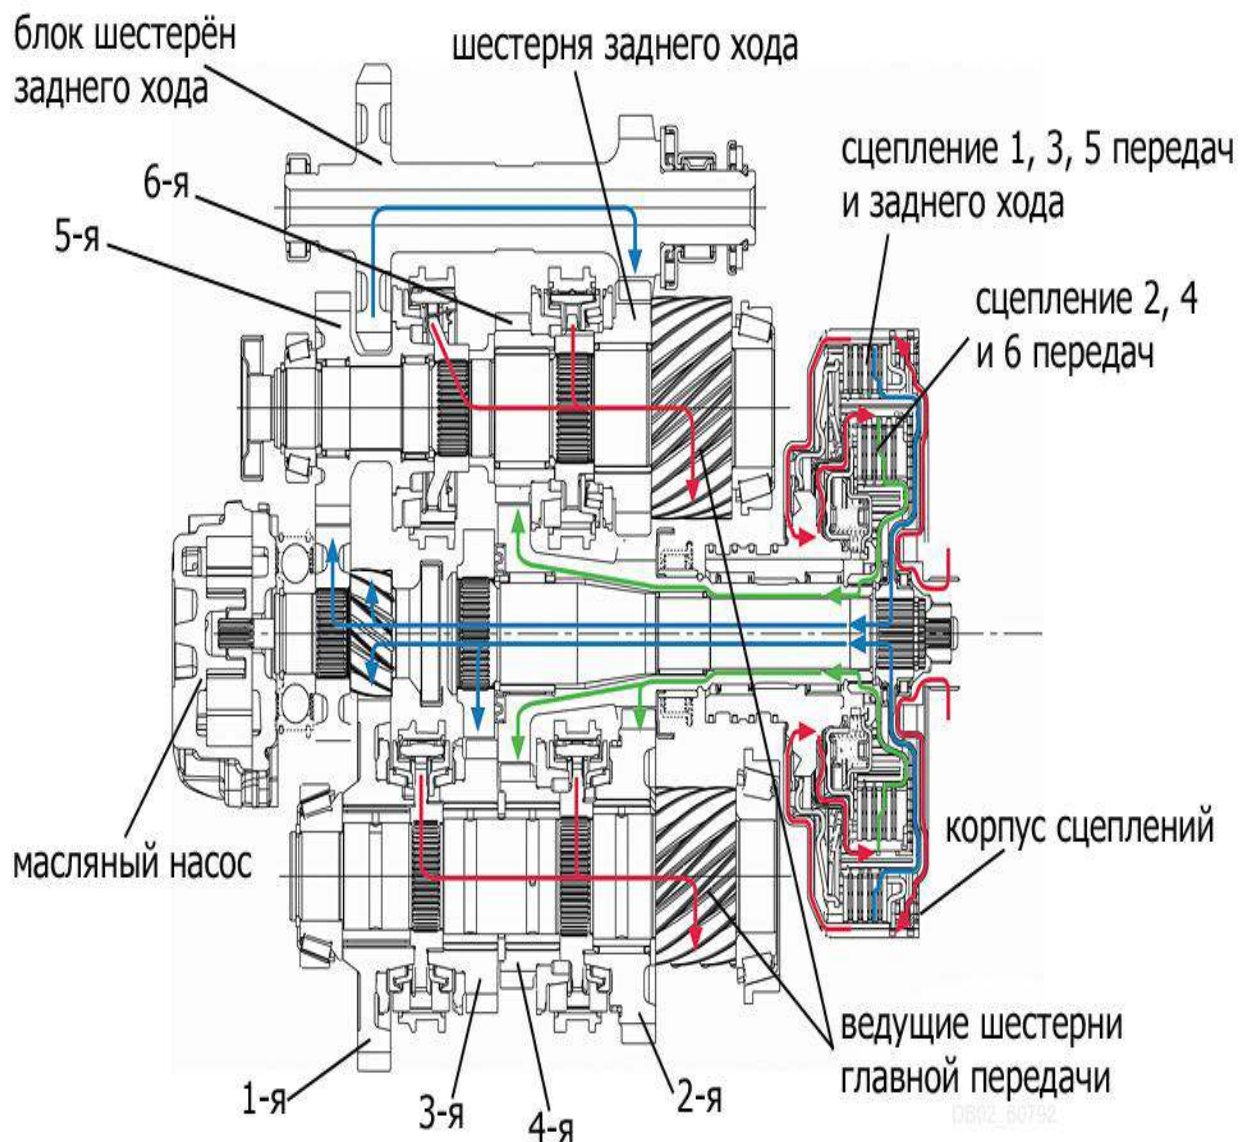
Схема четырехвальной коробки передач с двойным сцеплением
